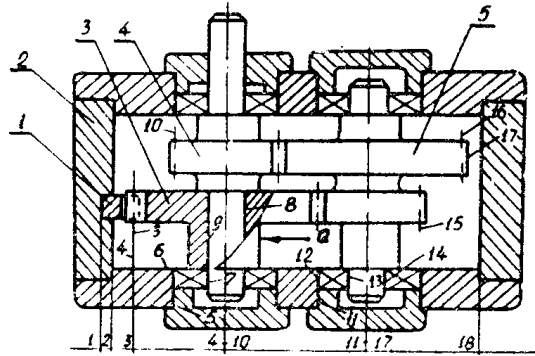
Зубчатый механизм: 1 — рейка, 2 — корпус, 3 — шестерня, 4 — трибка, 5 — двойчатка
